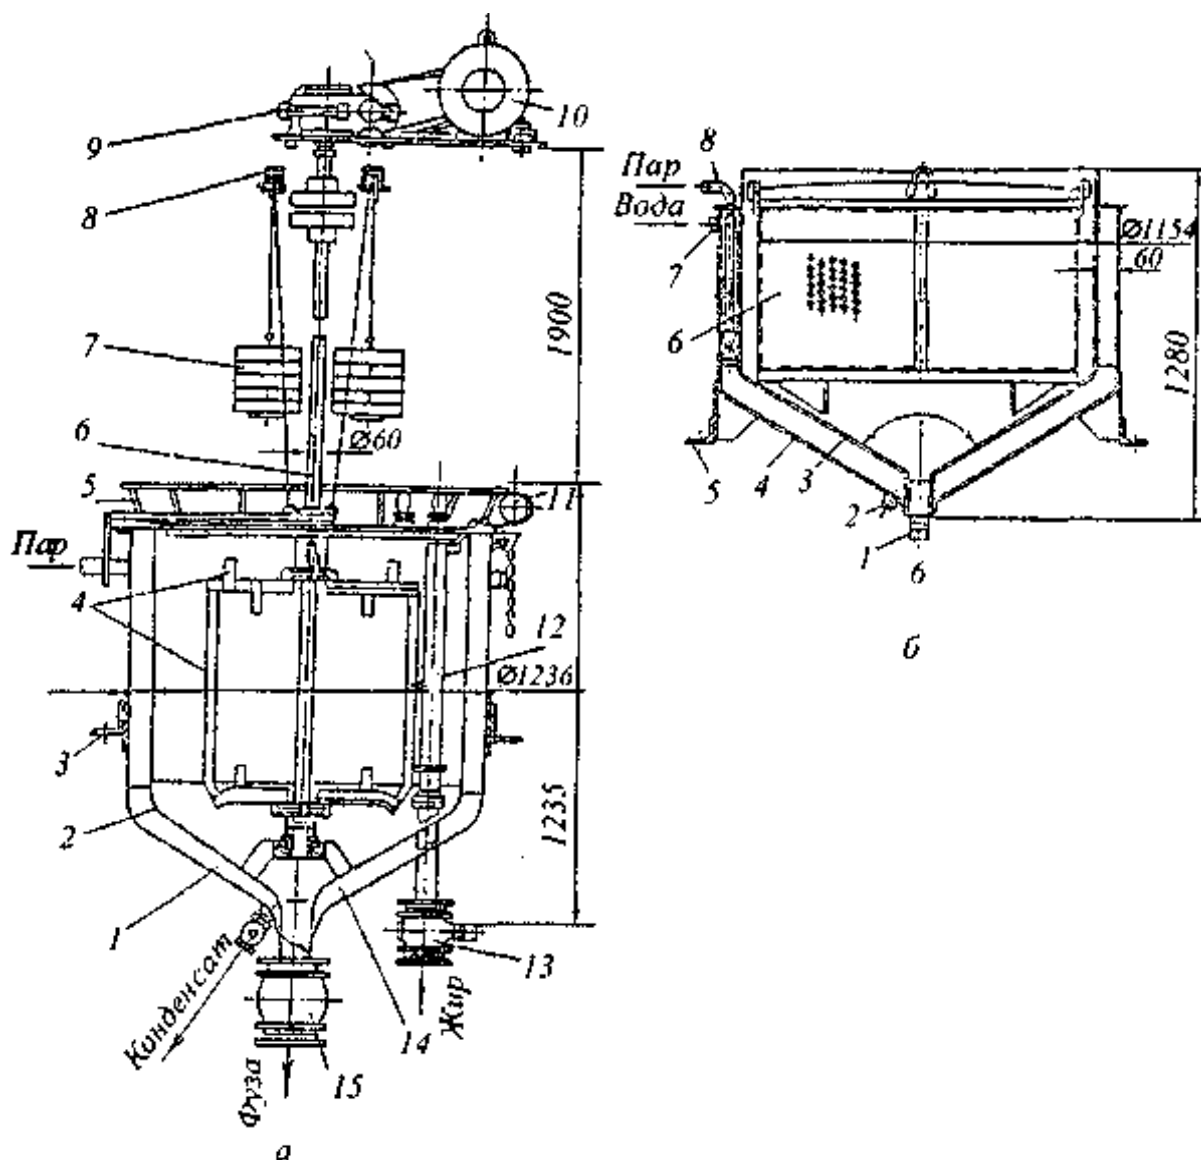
Відкриті котли: а – котел ОПК-1,25: 1 – зовнішній корпус, 2 – внутрішній корпус, 3 – опорні лапи, 4 – мішалка; 5 – огороження; 6 – вал; 7 – противага; 8 – блок; 9 – черв'ячний редуктор; 10 – електродвигун; 11 – манометр, 12 – поворотна труба; 13 – вентиль для зливу жиру; 14 – радіально-упорний підшипник; 15 – вентиль для зливу фузу; б – котел з виймальною кошиком: 1 – штуцер для зливу бульйону, 2 – штуцер для зливу конденсату; 3,4 – внутрішня і зовнішня обичайки; 5 – опорна лапа, 6 – кошик; 7,8 – труби для гарячої води і пари
